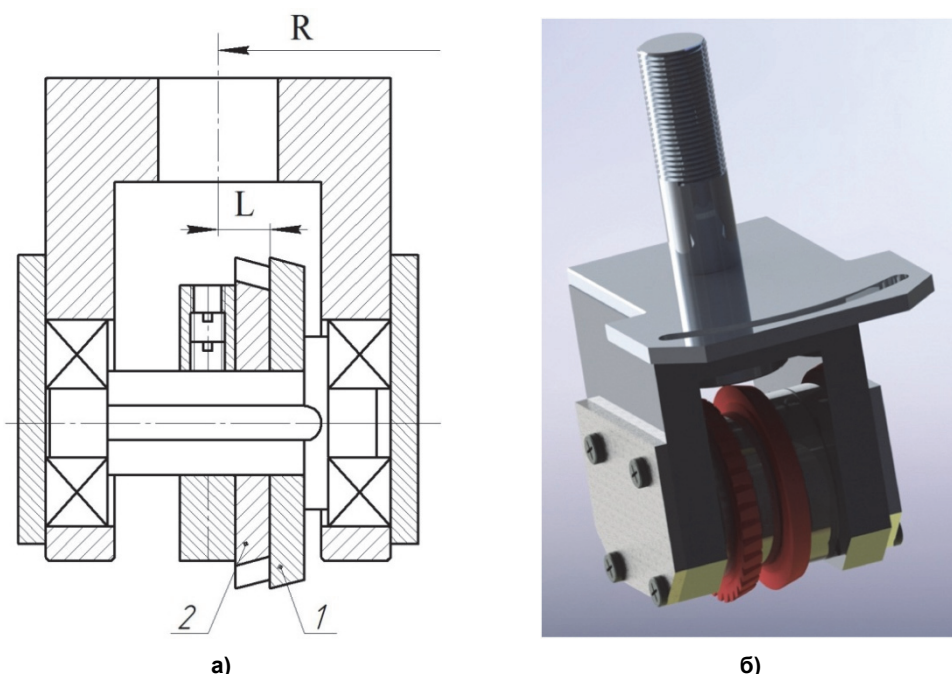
Режущий блок ротационной фрезы (а) и его 3D модель (б):
